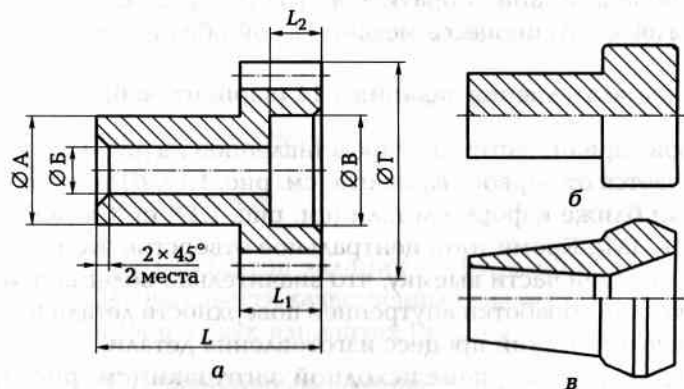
Зубчатое колесо (а) и варианты (б и в) заготовки для колеса
